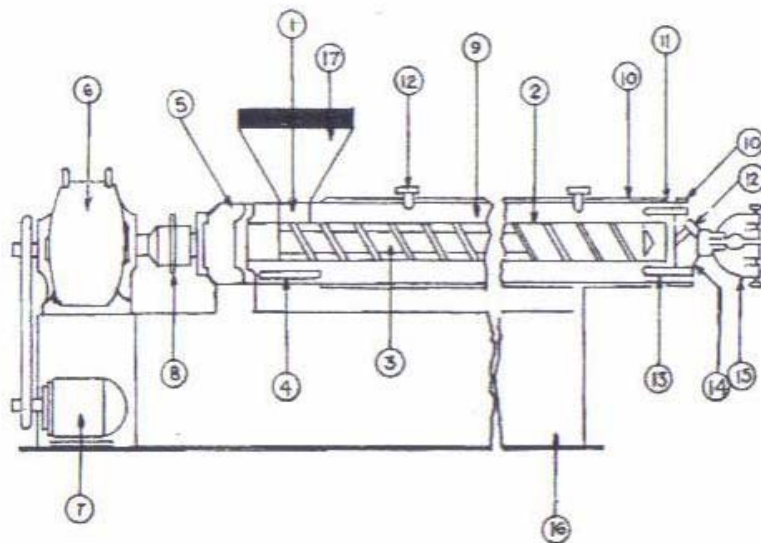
Partes principales de un extrusor de Filamento o pellet
